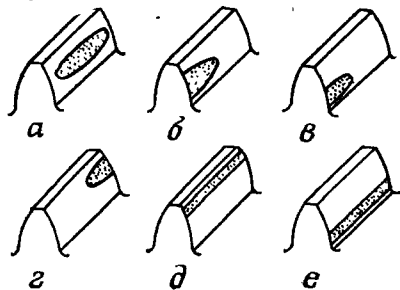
Проверка зацепления цилиндрических зубчатых пар по отпечаткам краски
